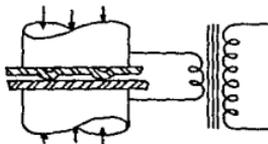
Principio de soldadura con salientes.
